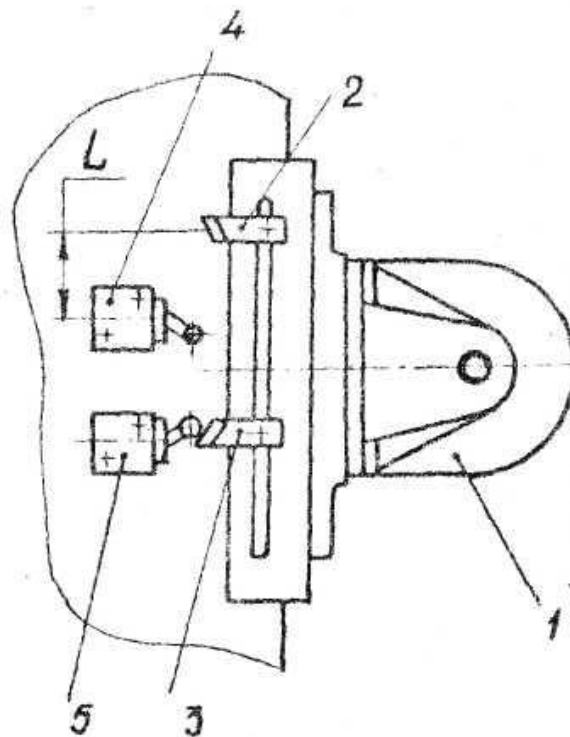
Схема встановлення упорів, що обмежують довжину ходу фрезерного супорту
